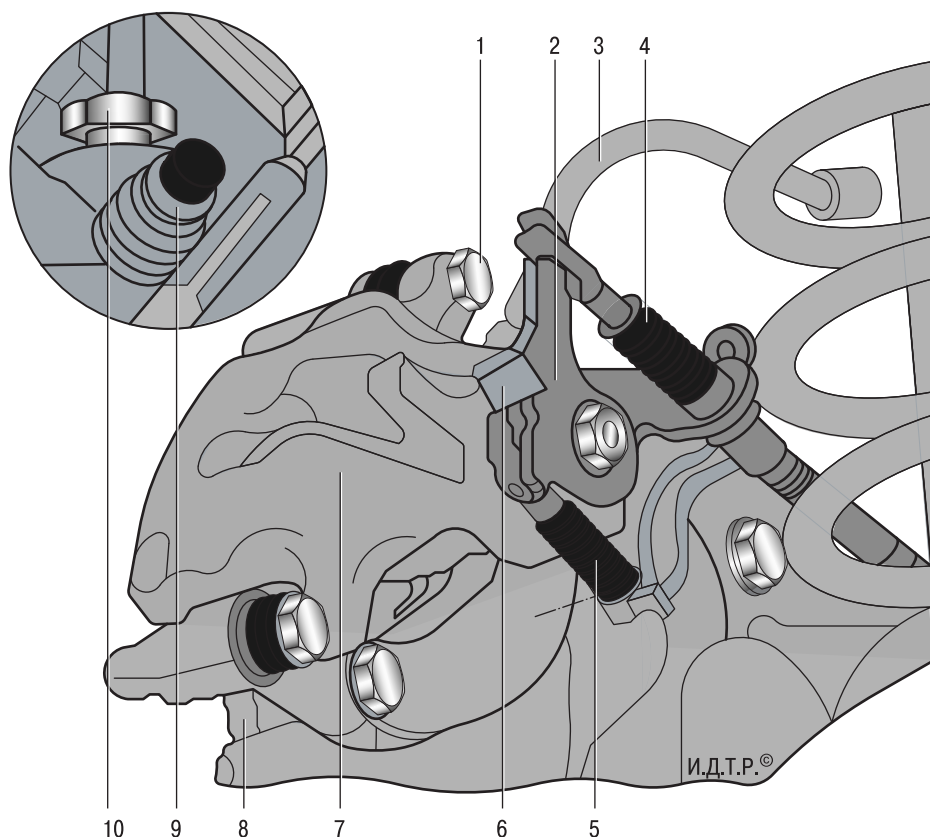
Дисковый тормозной механизм заднего колеса: 1 – направляющий палец; 2 – рычаг стояночного тормоза; 3 – гибкий тормозной шланг; 4 – трос стояночного тормоза; 5 – возвратная пружина стояночного тормоза; 6 – упор рычага стояночного тормоза; 7 – суппорт; 8 – тормозной диск; 9 – клапан удаления воздуха; 10 – гайка наконечника тормозного шланга
